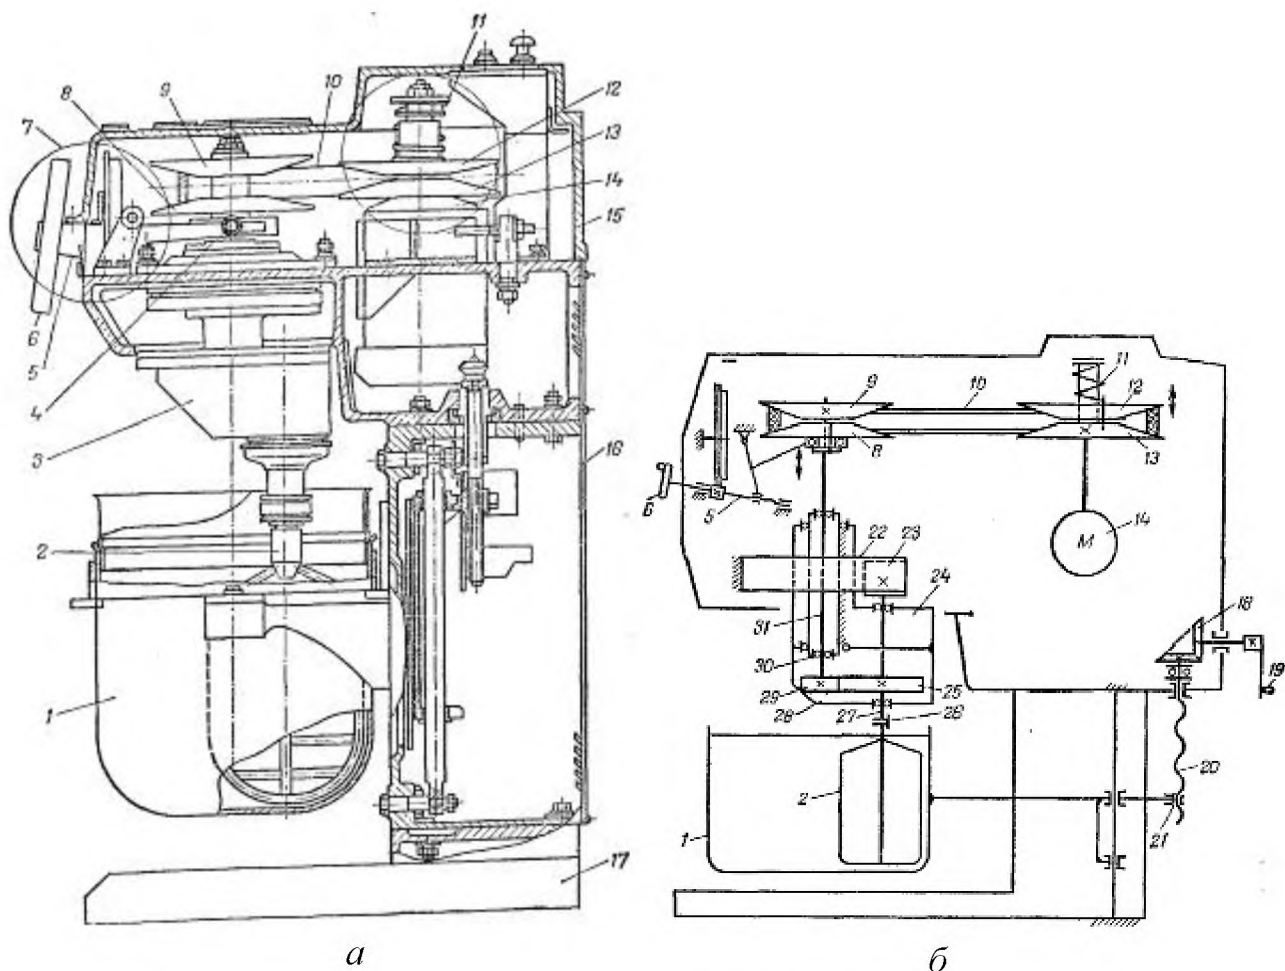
Машина МВ-35: а – вигляд загальний; б – схема кінематична; 1 – бачок; 2 – збивач; 3 – головка; 4 – сухарі; 5 – гвинт ходовий; 6 – маховик; 7 – механізм регулювання швидкості обертання робочого органа; 8 – напівшків нижній ведений; 9 – напівшків верхній ведений; 10 – пас; 11 – пружина; 12 – напівшків верхній провідний; 13 – напівшків нижній провідний; 14 – електродвигун; 15 – головка; 16 – станина; 17 – основа; 18 – конічна зубчаста передача; 19 – рукоятка; 20 – ходовий гвинт; 21 – гайка; 22 – сонячне колесо; 23 – сателіт; 24 – водило; 25 – зубчасте колесо; 26 – гільза; 27 – вал; 28 – кришка алюмінієва; 29 – шестерня; 30 – підшипник; 31 – вал
